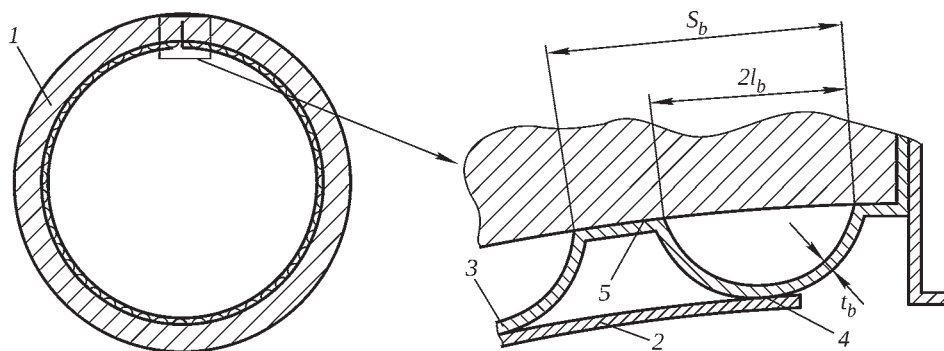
Конструкция радиального газодинамического подшипника первого поколения:
